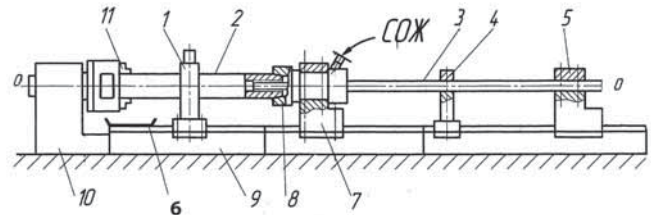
Схема наладки горизонтально – сверлильного станка на растачивание цилиндров: 1 – люнет; 2 – заготовка; 3 – стембель; 4 – стембевый люнет; 5 – каретка подач; 6 – стружкоприемник; 7 – передняя стойка; 8 – маслоприемник; 9 – станина; 10 – передняя (шпиндельная) бабка
